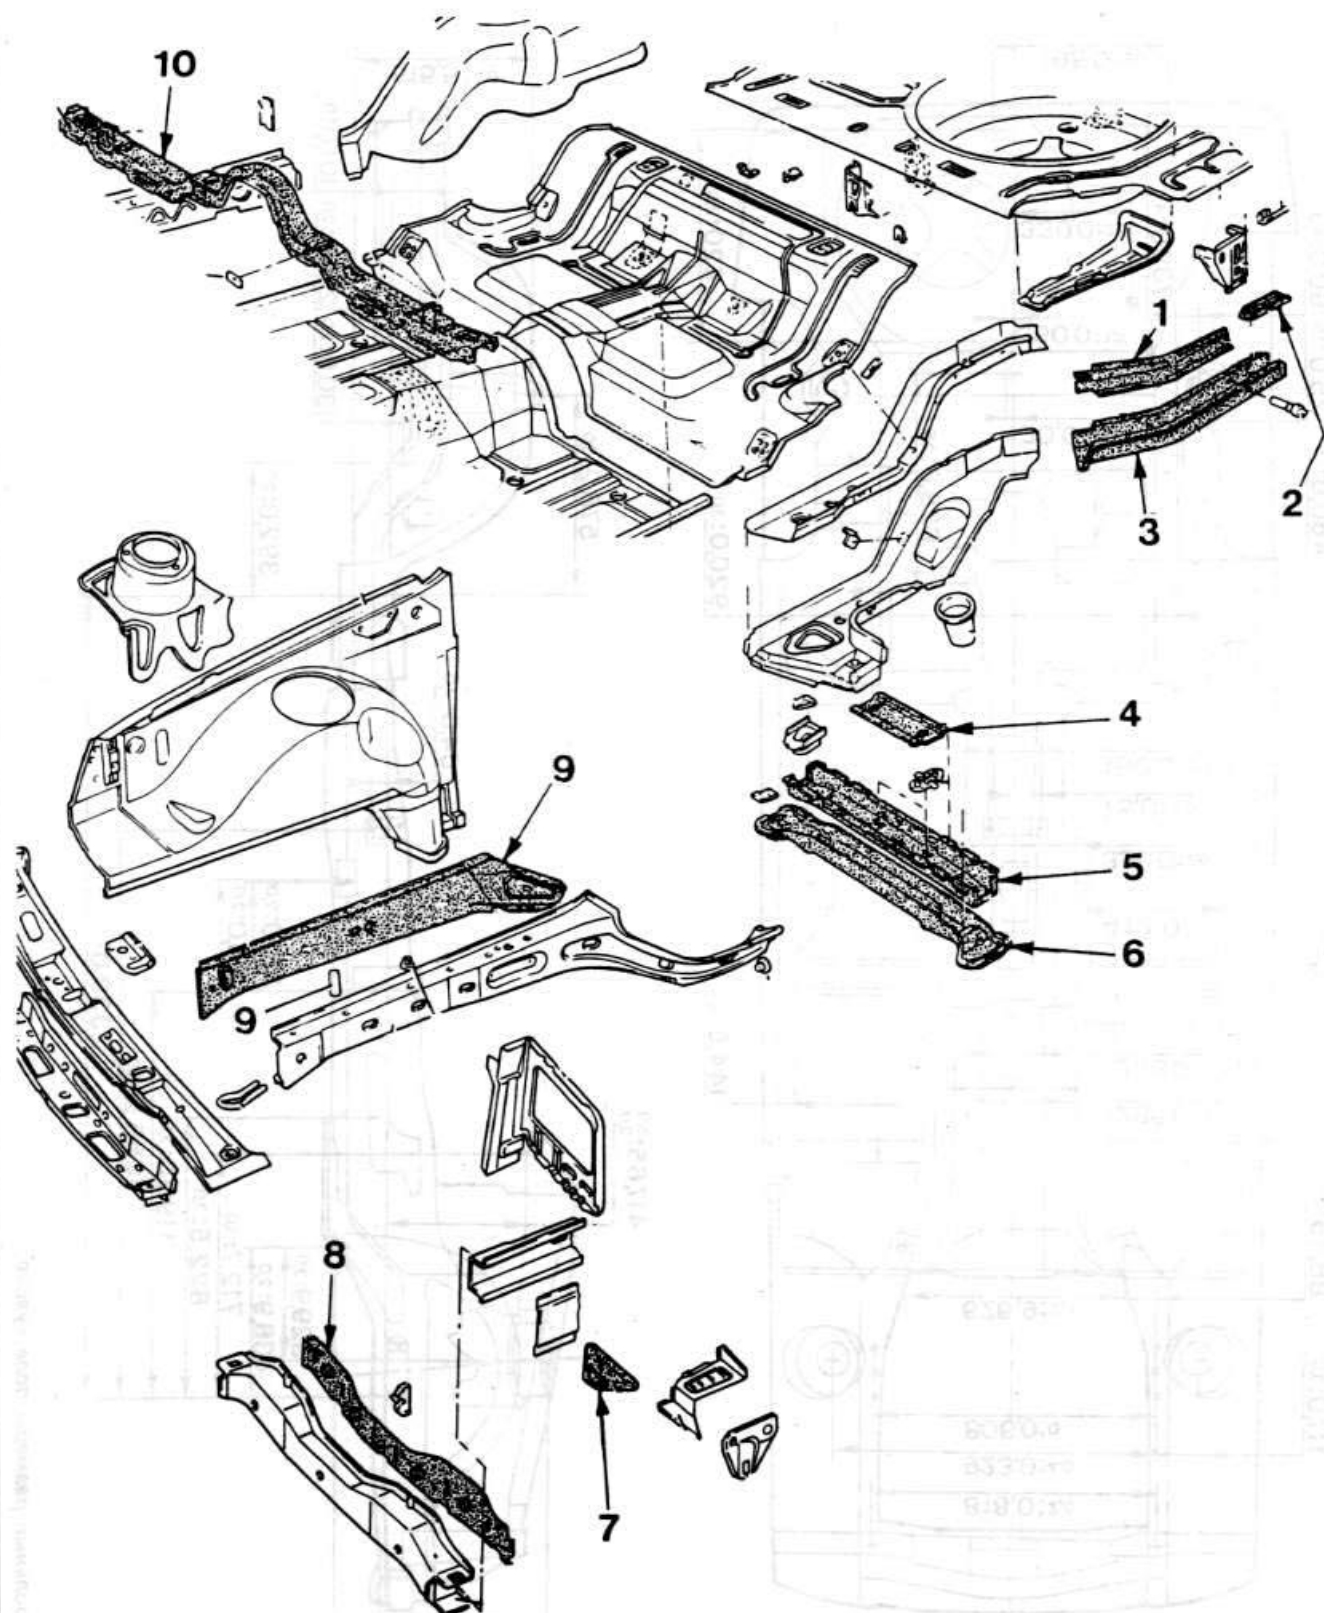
Детали кузова, изготовленные из спецсталей:
